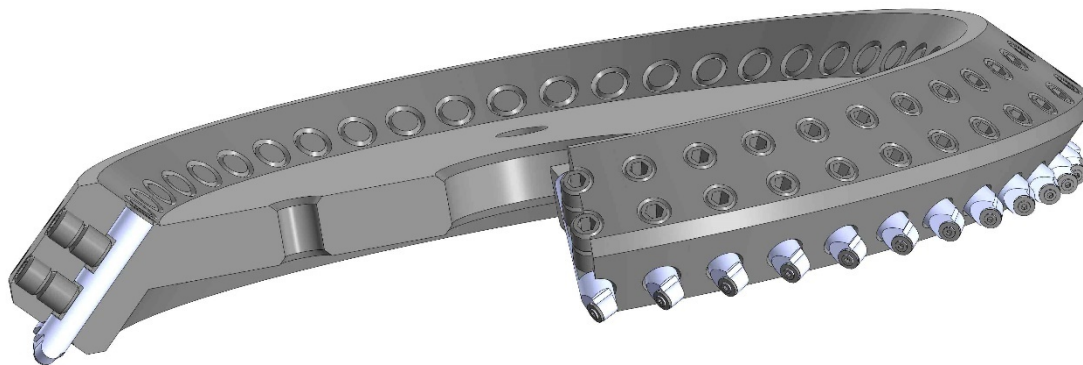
Торцева фреза з додатковими стопорними гвинтами
